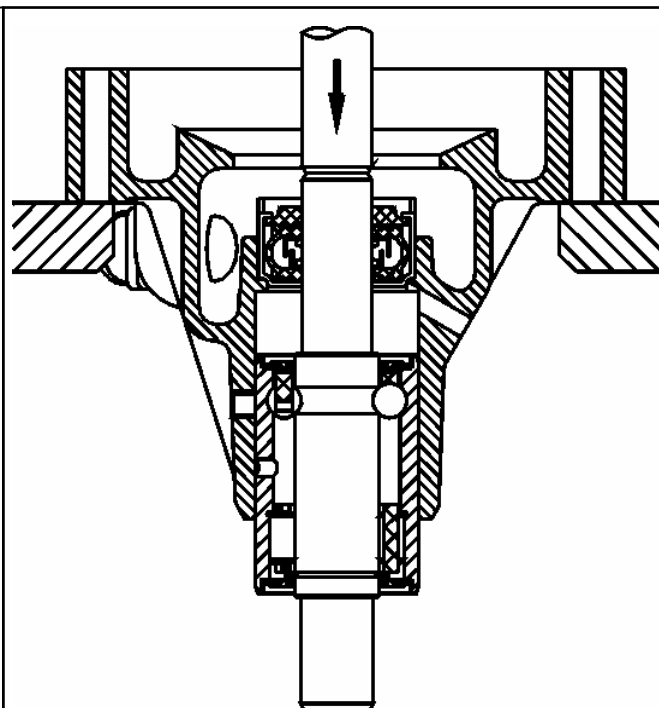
Выпрессовка подшипника в сборе с валиком из корпуса насоса
